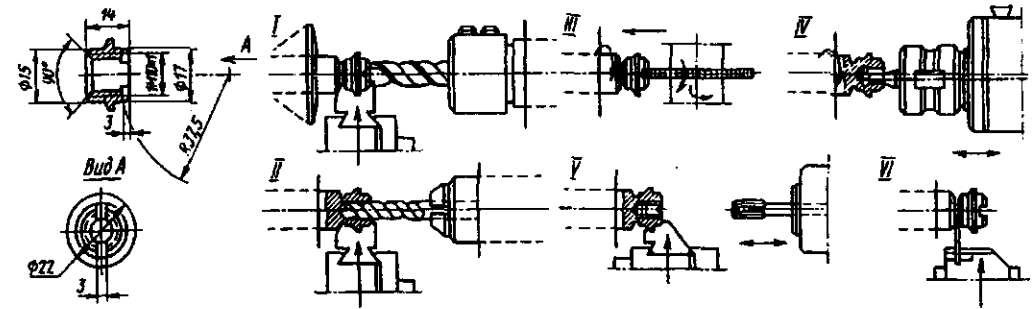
Наладка шестишпиндельного автомата для обработки специальной гайкой с использованием приспособления для фрезерования шлица
